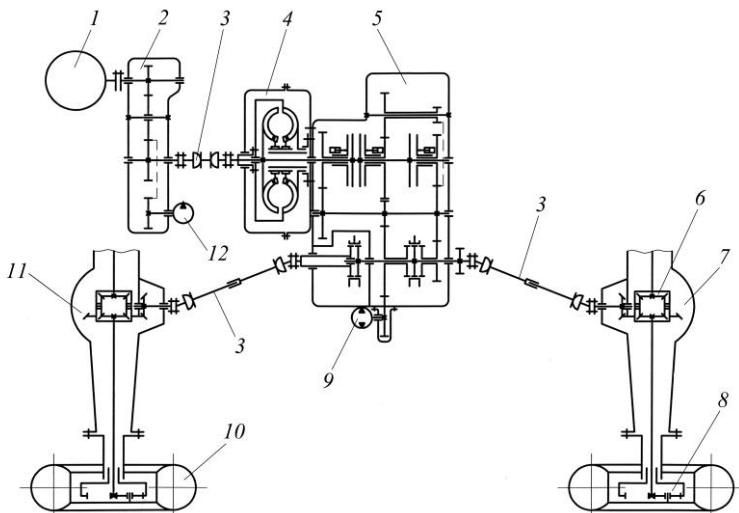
Кинематическая схема двухосного шасси колесного погрузчика:
